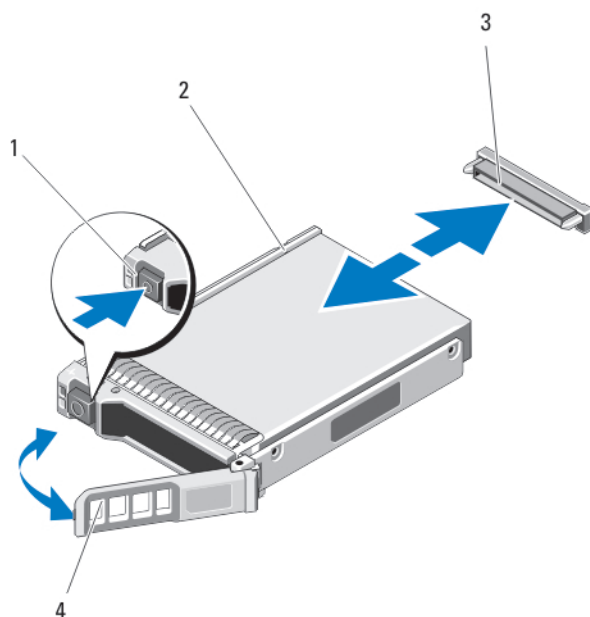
Festplatten-/SSD-Laufwerk entfernen und installieren
